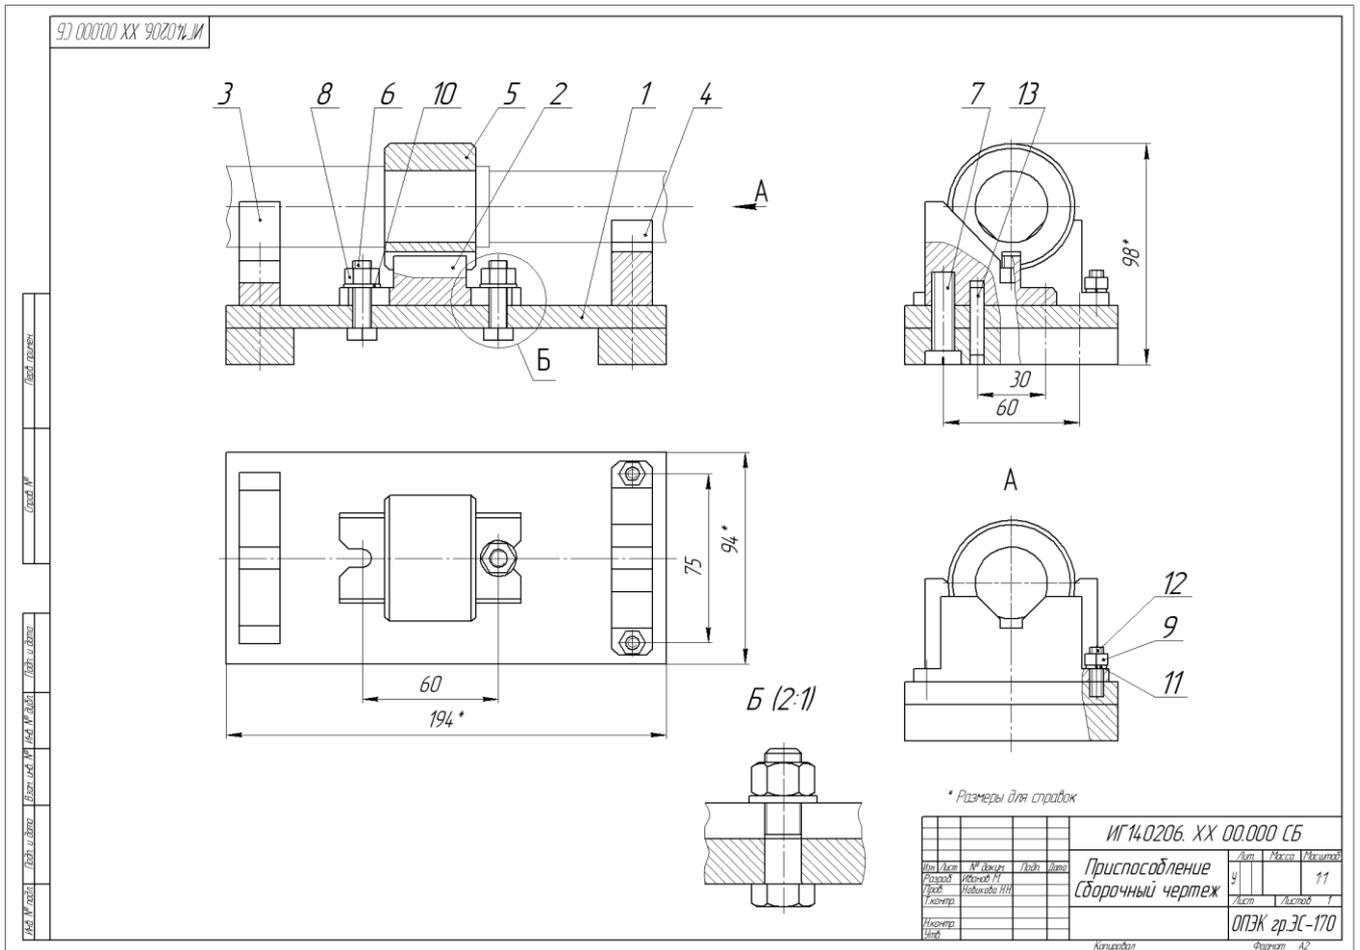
Сборочный чертеж сборной единицы «Приспособление»
